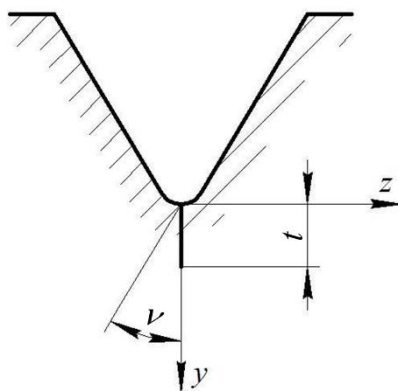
Трещина усталости в резьбовой детали
